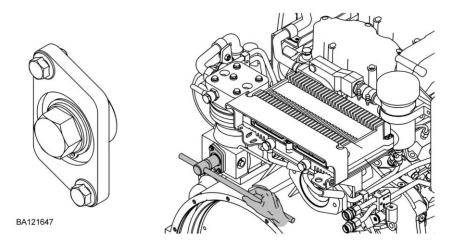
Dispositivo de giro: montaje del compresor para salida secundaria, herramienta especial Nr. 30b
